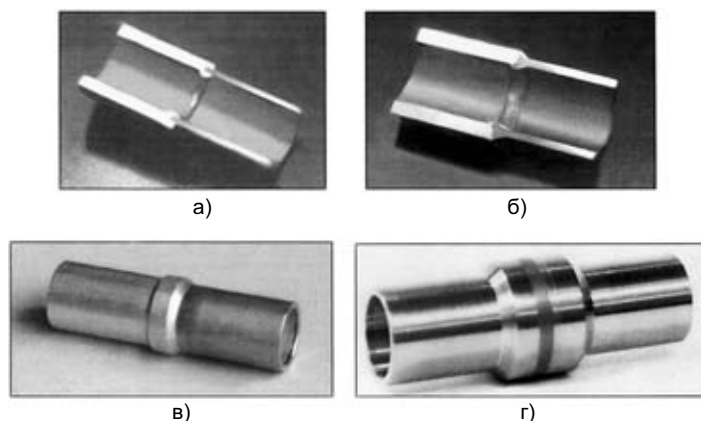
Сварные соединения трубных переходников: а — разрез сварного соединения трубы из сплава АМг2 сечением ($d \times \delta$) $1,4 \times 2$ мм и трубы из стали 12Х18Н10Т сечением 12×1 мм; б — разрез сварного соединения трубы из сплава АМг2 сечением 14×2 мм и трубы из титана ВТ1 сечением 12×1 мм; в — трубный переходник АМг2 + 12Х18Н10Т ($d_y = 10$ мм); г — трубный переходник 12Х18Н10Т + ВТ6С ($d_y = 19$ мм)
